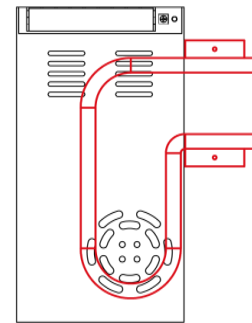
Vista en planta de la fuente de alimentación con la pieza (rojo).
